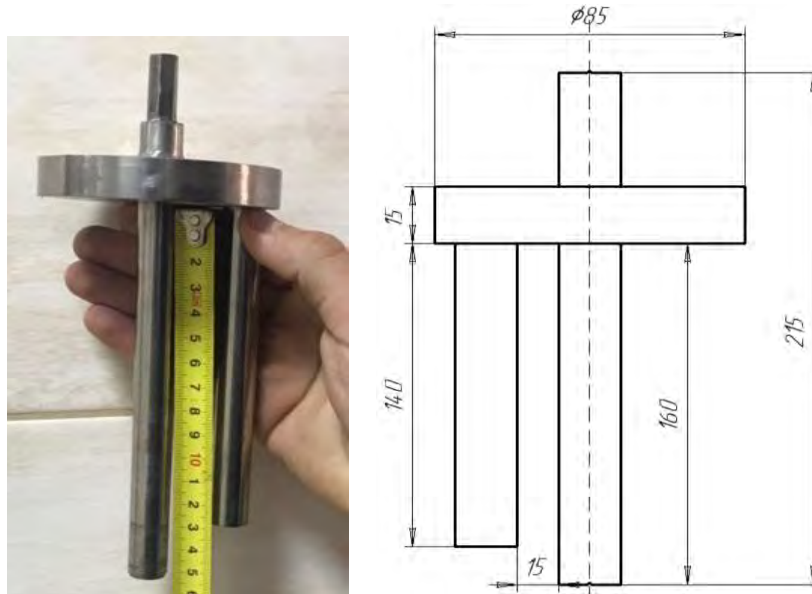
Вилка (фото) и ее геометрические размеры
